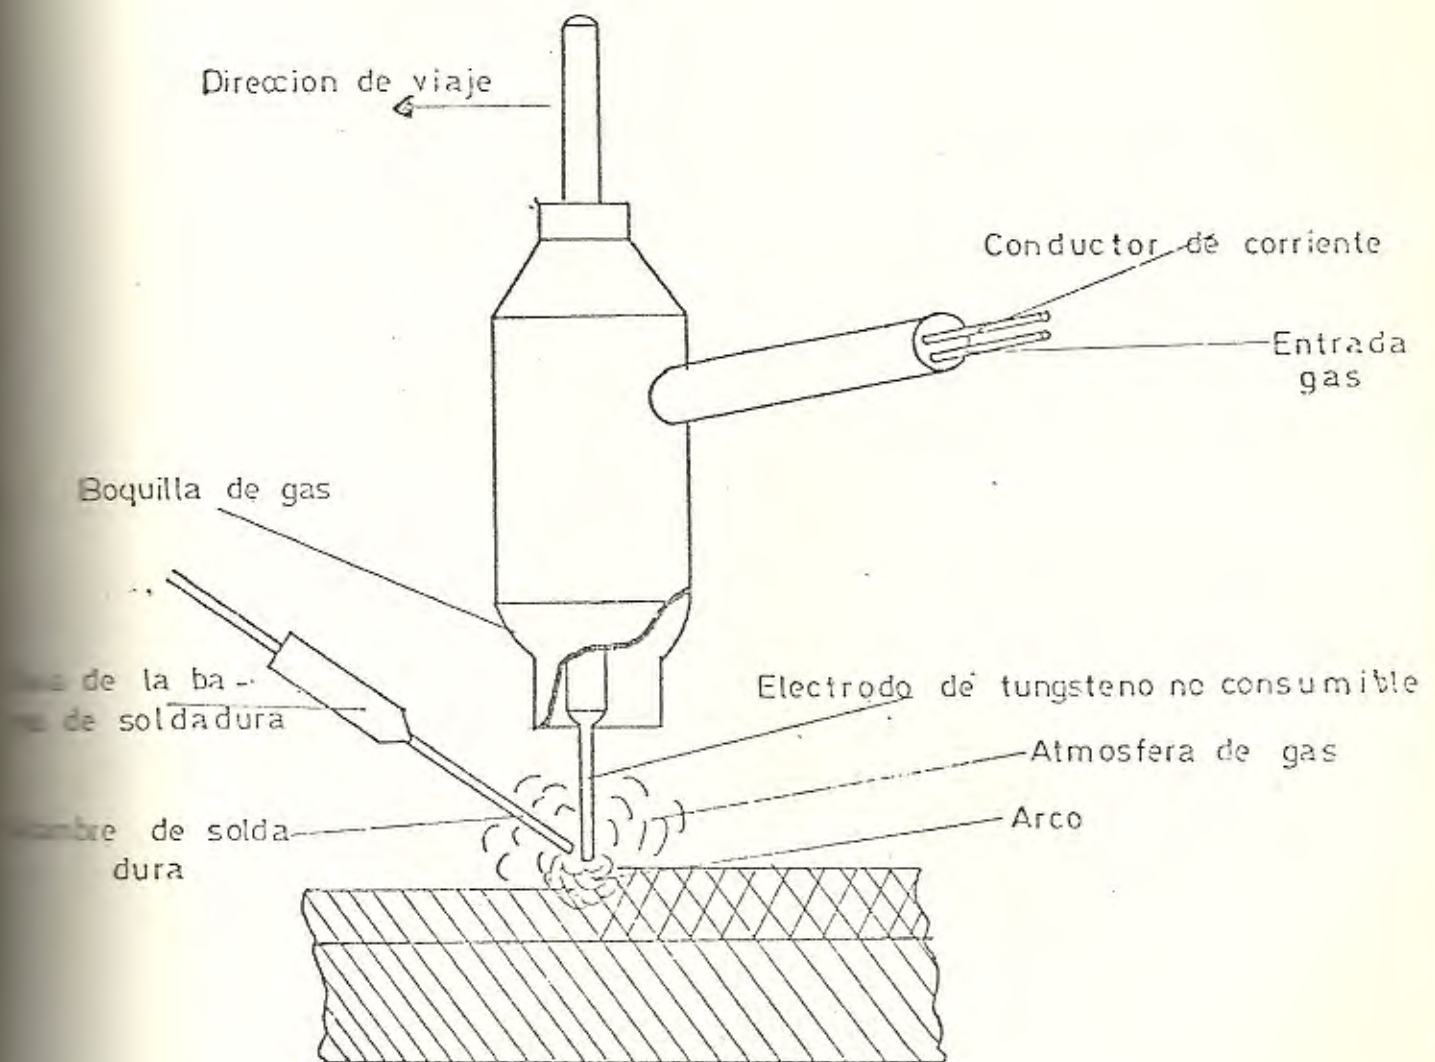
SOLDADURA AL ARCO CON GAS PROTECTOR
